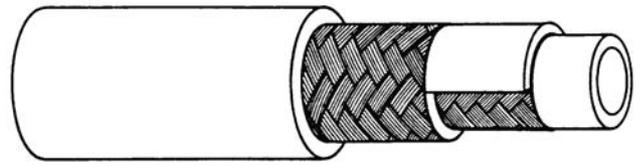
Schlauch mit geflochtenem Druckträger (2-lagig)
